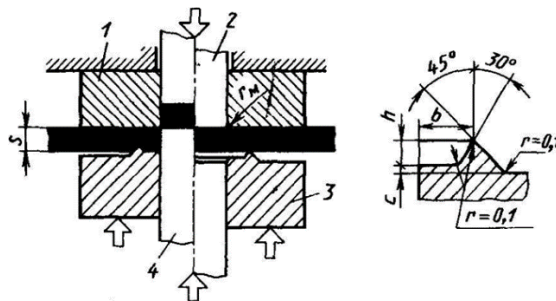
Рабочий инструмент для чистовой вырубки с предварительным сжатием
